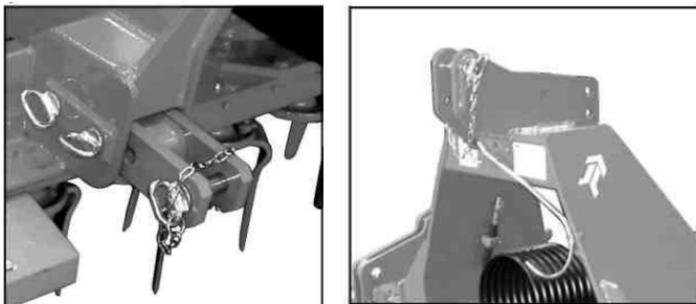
Сцепка фрезерного культиватора с трактором
